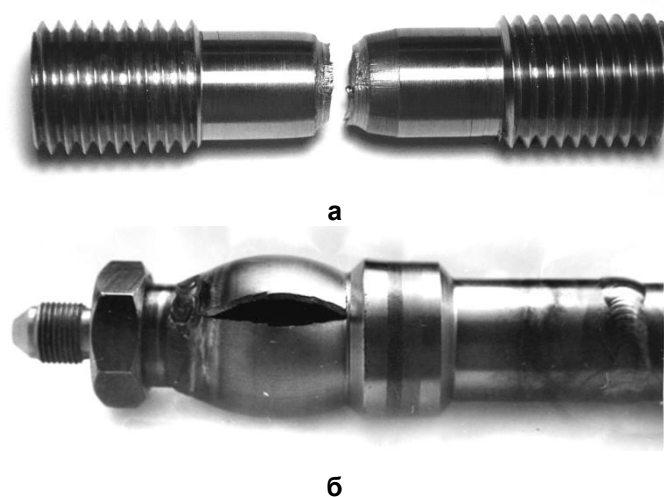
Внешний вид сварной заготовки сталь-титан сечением  $\varnothing 20 \times 7$  мм после испытания на статическое растяжение (а) и трубного переходника ( $d_y = 19$  мм) после испытания на прочность внутренним давлением (б)
